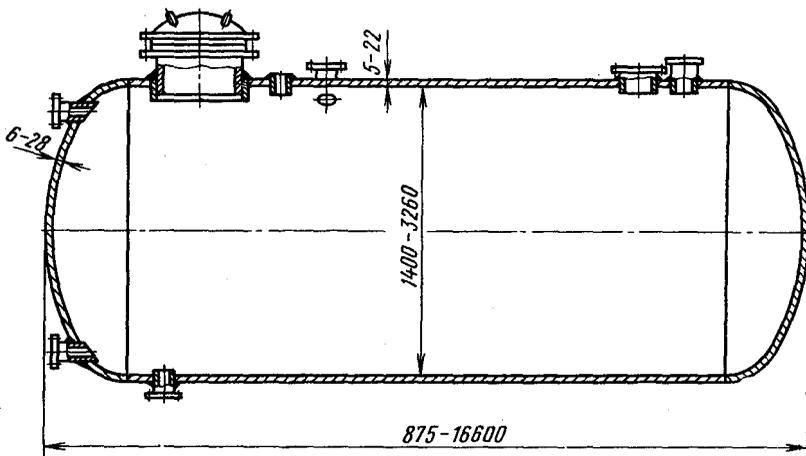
Конструкция резервуара с эллиптическими отбортованными днищами
